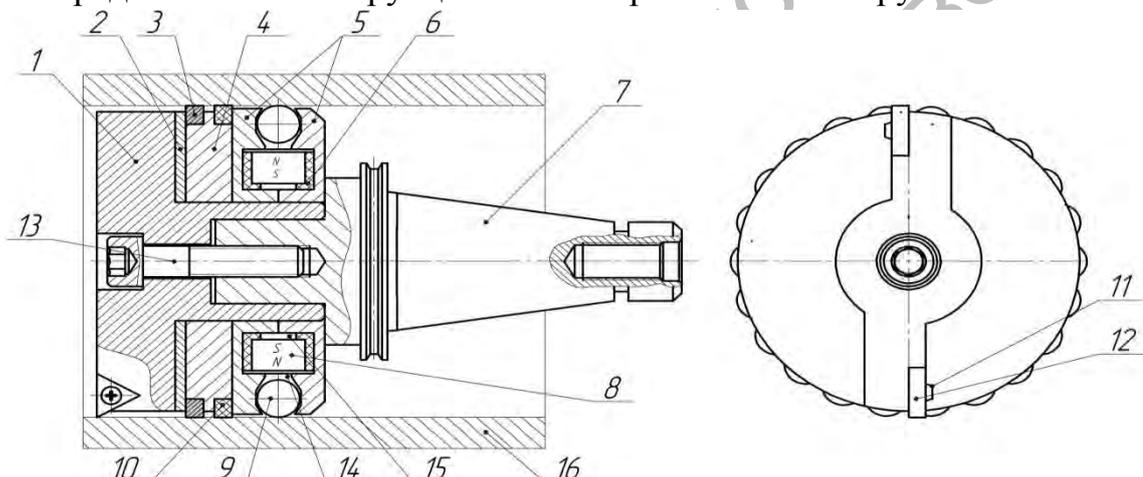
Конструкция комбинированного магнитно-динамического раскатника: 1 – расточная головка; 2 – уплотняющее кольцо; 3 – щётка; 4 – втулка; 5 – диски; 6 – обойма; 7 – фрезерная оправка; 8 – источники магнитного поля (цилиндрические постоянные магниты); 9 – деформирующие элементы; 10 – фетровая втулка; 11 – винт; 12 – твердосплавная режущая пластина; 13 – винт; 14 – кольцевая камера; 15 – радиальные отверстия; 16 – деталь.
